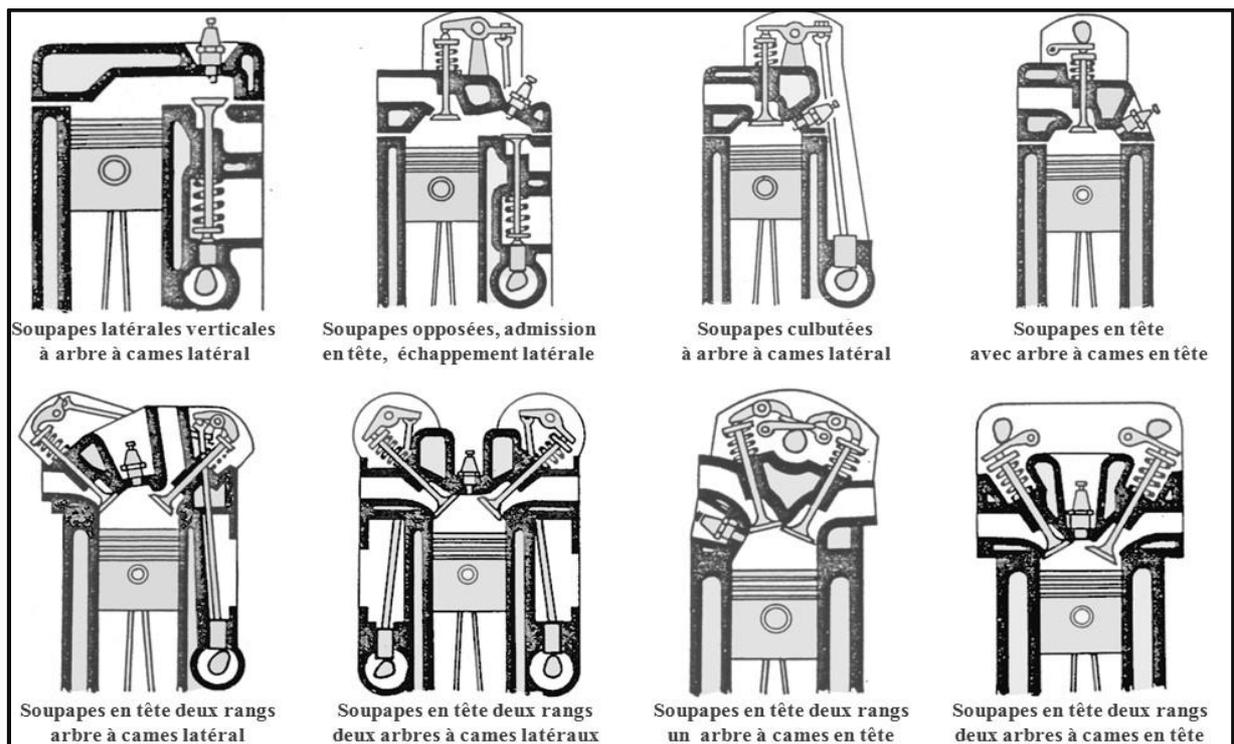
Disposition des soupapes et arbres à cames [3].
